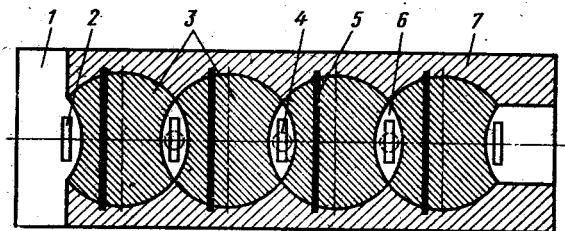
Установка полунепрерывного действия линейной компоновки с полуоткрытой шлюзовой системой:
